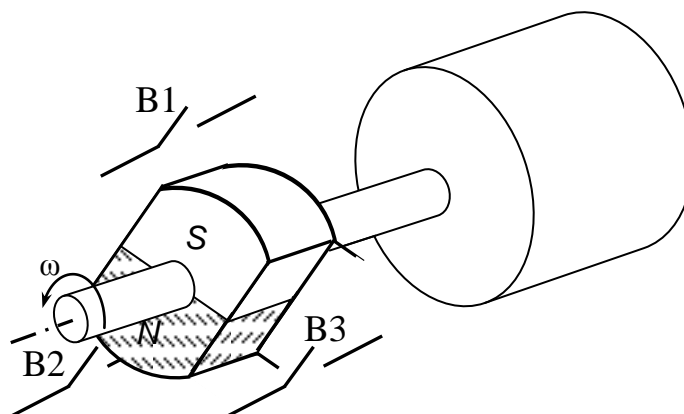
Схема конструкции датчика положения ротора и его расположение на валу двигателя
